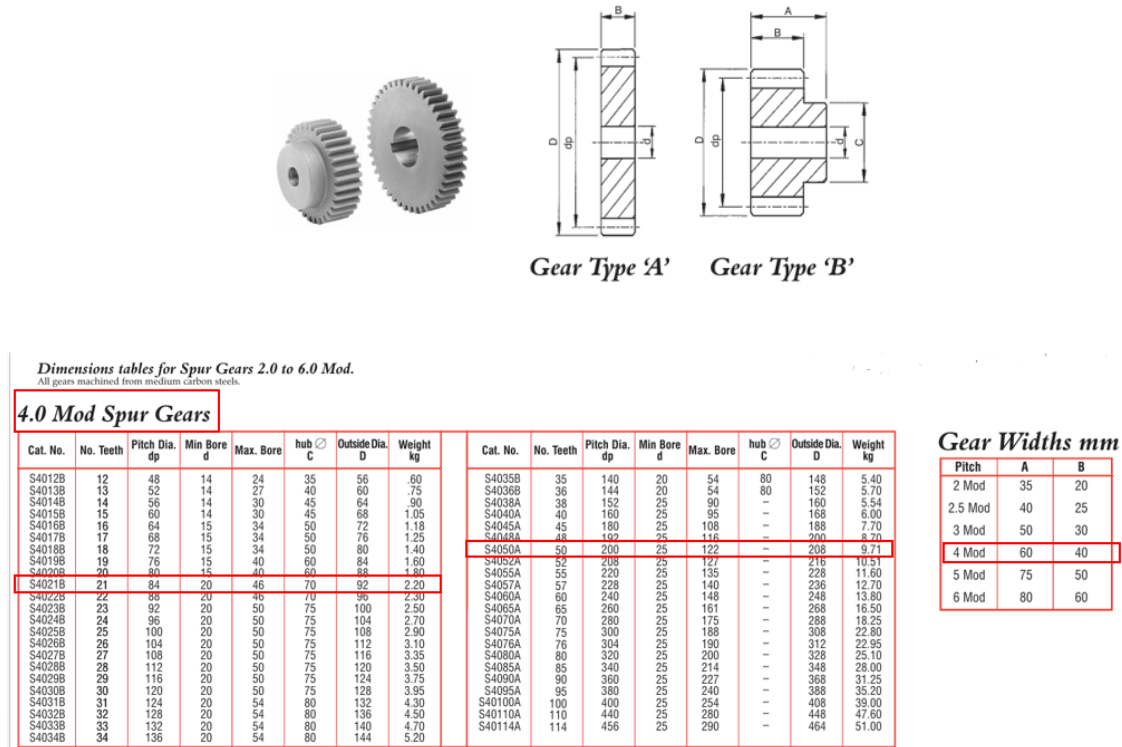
Catálogo estándar de engranajes rectos [5].
